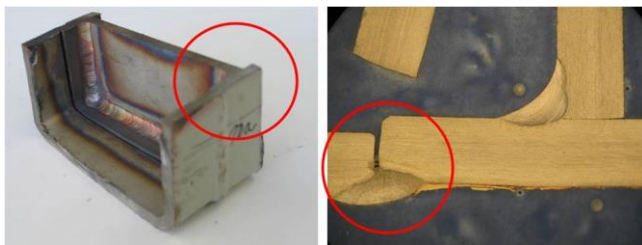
links ausgeführte Schweißung Vierkantrrohr - rechte Seite dazugehöriges Schlibfbild
